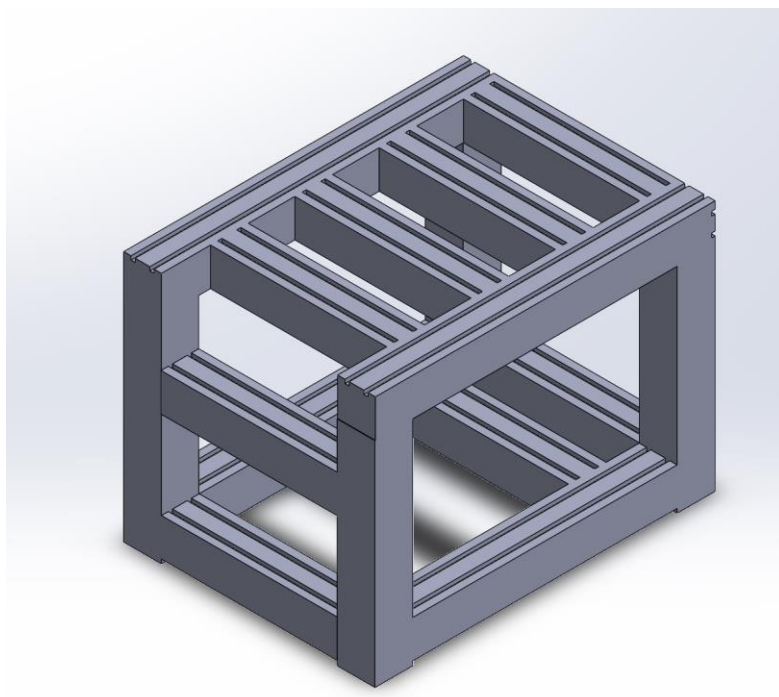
Estrutura em perfil Bosch final noutra perspetiva
